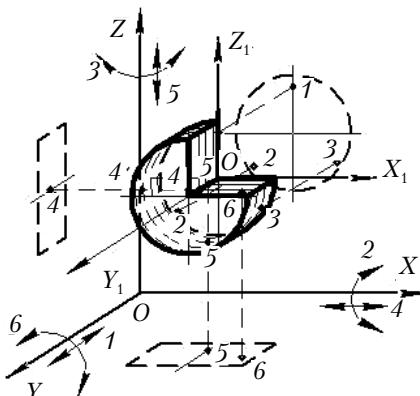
Схема базирования заготовки по короткой цилиндрической поверхности
